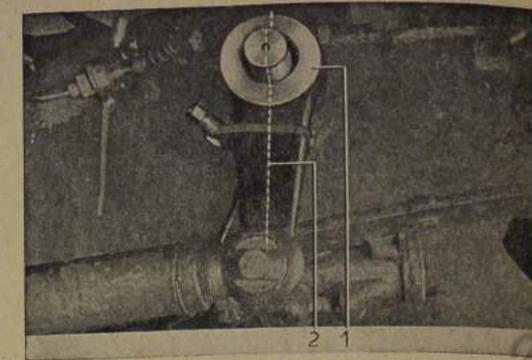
Lenkstockhebel senkrecht nach unten zeigend aufschieben
